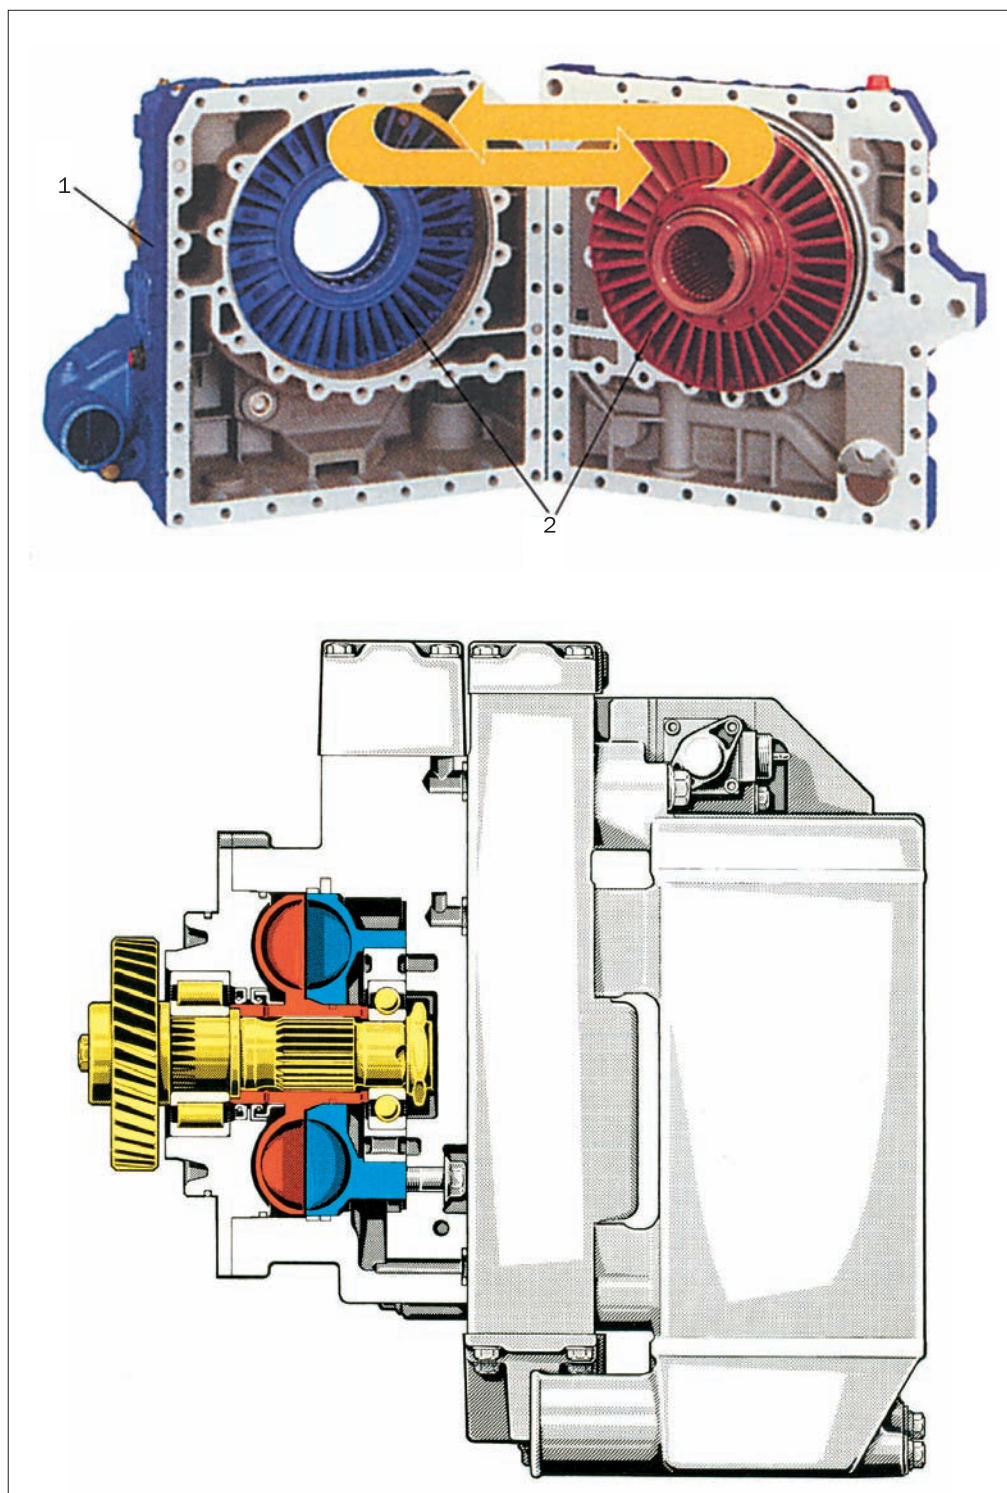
Гидравлический тормоз-замедлитель: 1— корпус; 2 — лопастное колесо
